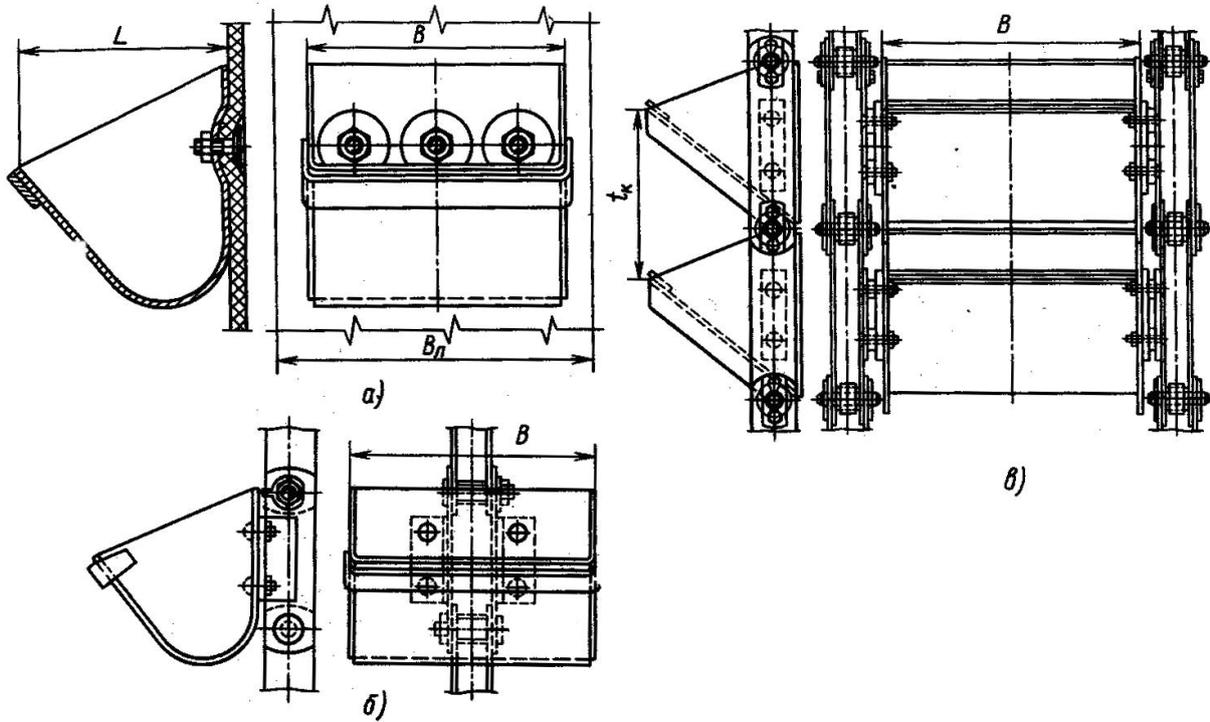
Крепление ковшей элеватора: а – к ленте; б – к одной цепи; в – к двум цепям
